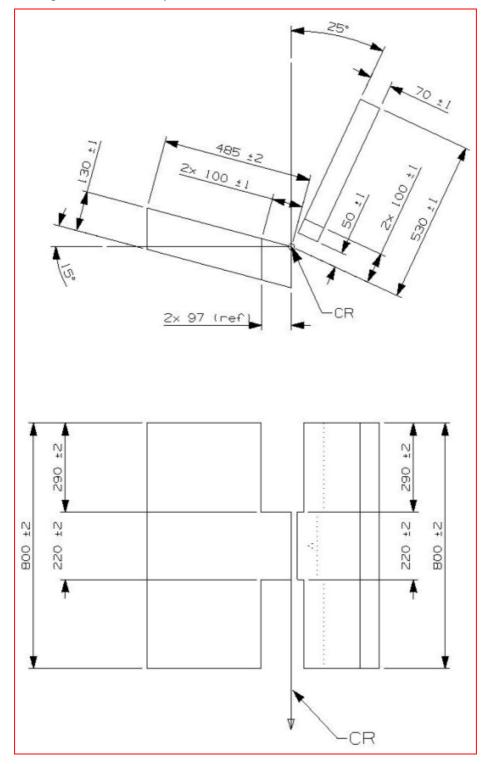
Размеры алюминиевой опорной пластины и размеры алюминиевой опорной пластины спинки сиденья
